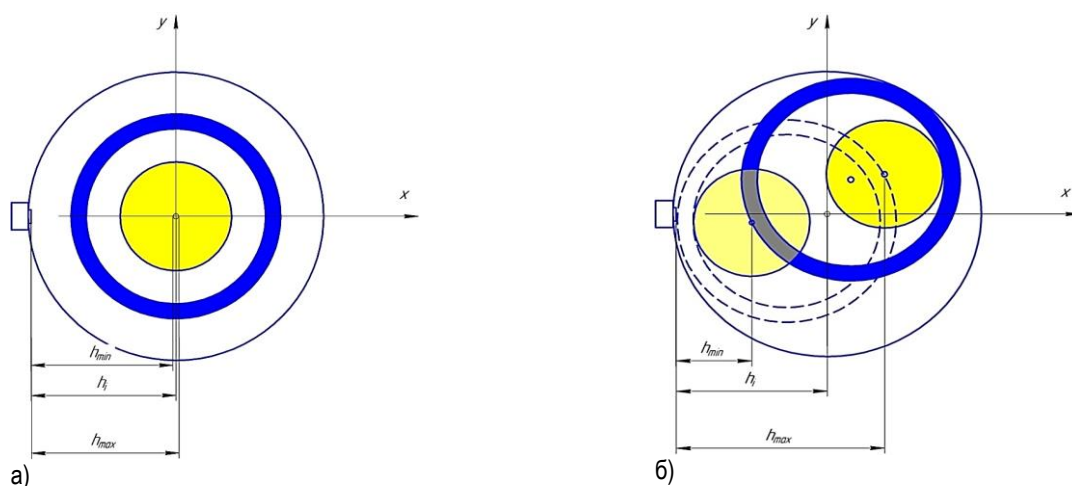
Расположение моноштулки и ротора в корпусе турбокомпрессора:
